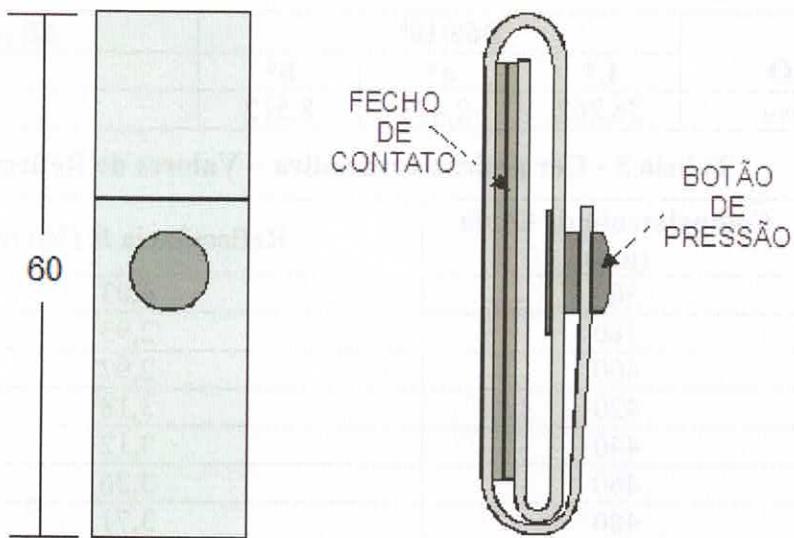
Detalhe de confecção do tirante de fixação ao cinto tipo NA(medidas em mm)
